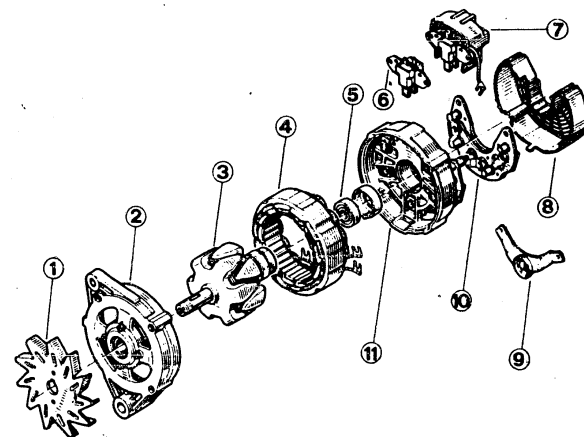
Alternator PARIS-RHONE: 1 Lüfter – 2 vorderes Gehäuse – 3 Rotor – 4 Stator – 5 Lager – 6 Schleifkohlenrührer – 7 Regler – 8 hinterer Gehäuse-Deckel – 9 Halter – 10 Diodenträger – 11 hinteres Gehäuse.
